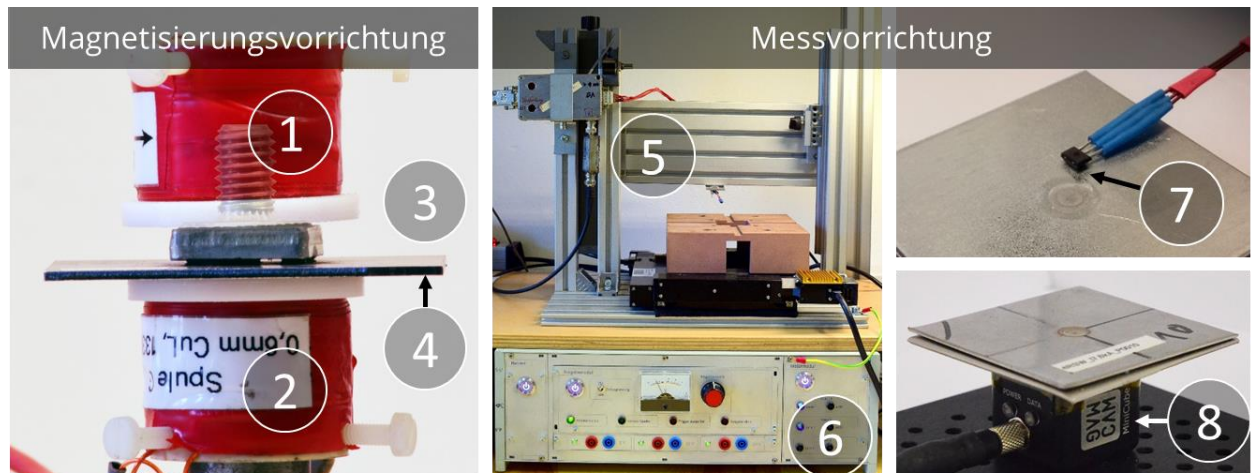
Messaufbau pMFT mit Darstellung der Magnetisieruvorrichtung mit den beidseitig angeordneten, gleichgerichteten Spulen (1, 2), der Buckelschweißverbindung mit dem Fügeelement (3), dem Blech (4); Messvorrichtung mit Kreuztisch (5); Steuerung für den Magnetisierungsprozess und Kreuztisch (6); Hallensensor (7) und 2D-Magnetfeldkamera (8)
